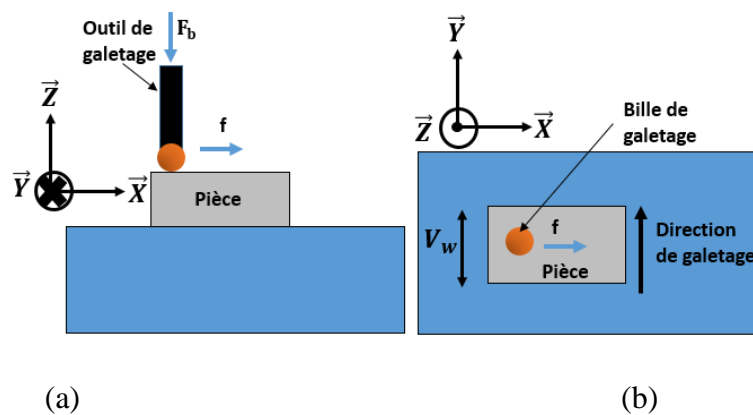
(a) Vue de face, (b) vue de dessus du procédé de galetage.
